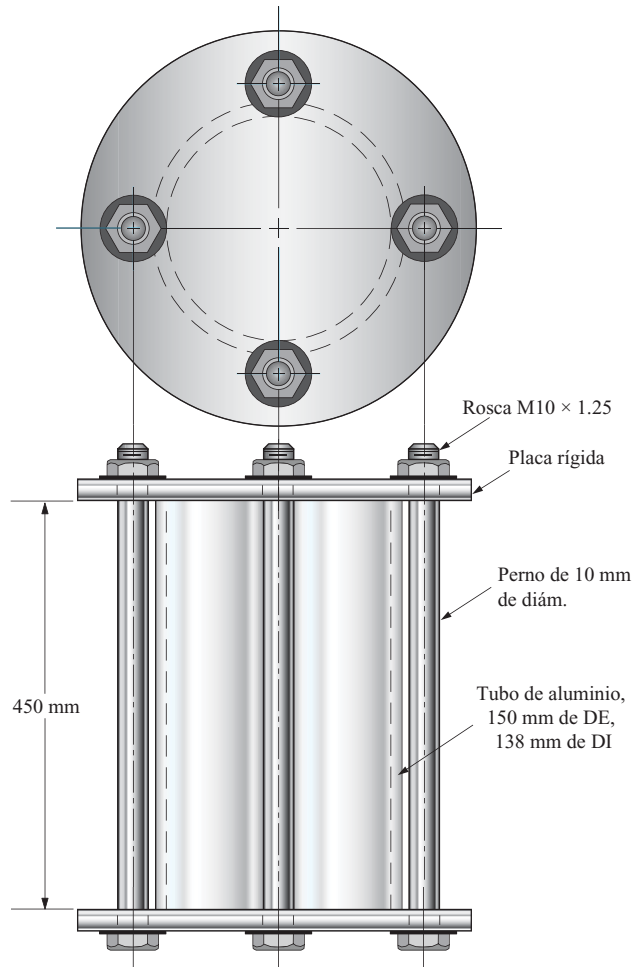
Tirantes en un cilindro del problema 3-73.
